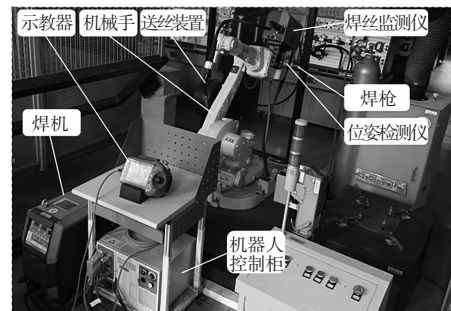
焊接机器人样机故障诊断模拟试验现场
